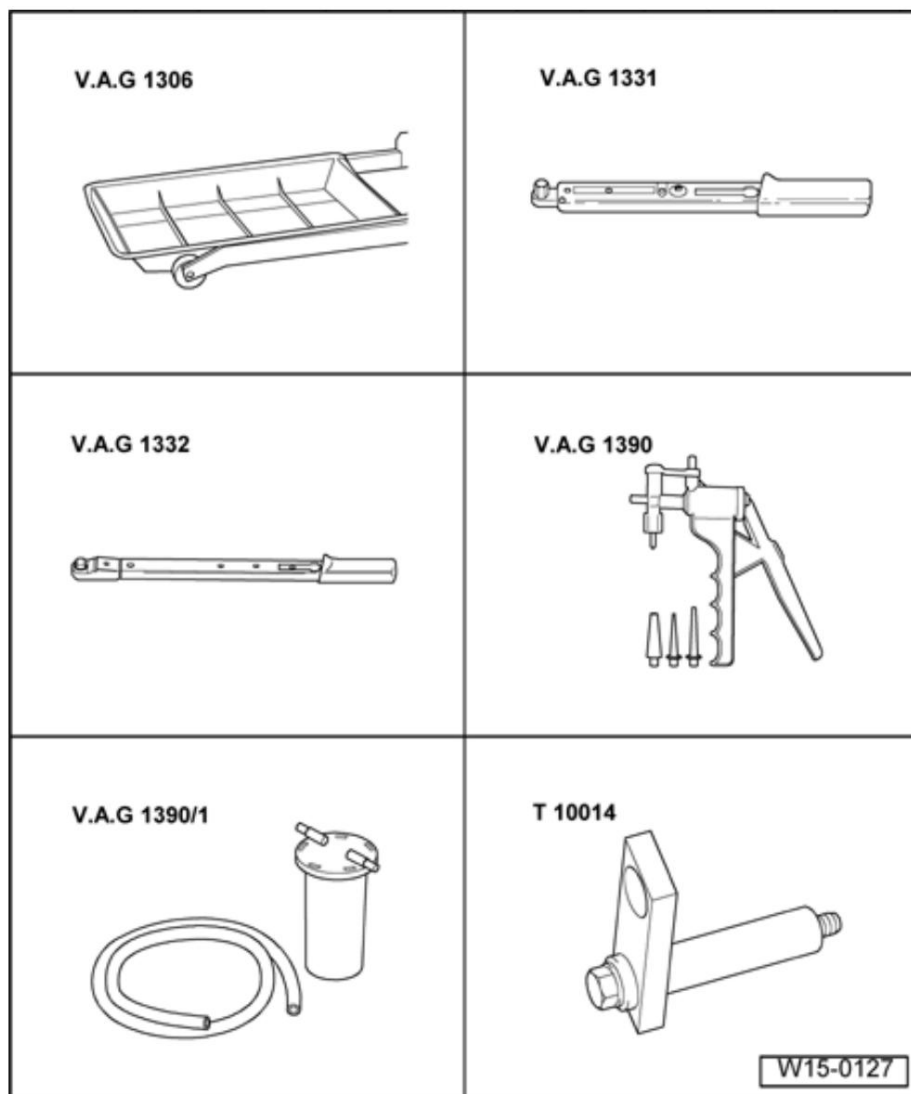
Herramientas especiales - Culata, desmontaje y montaje
